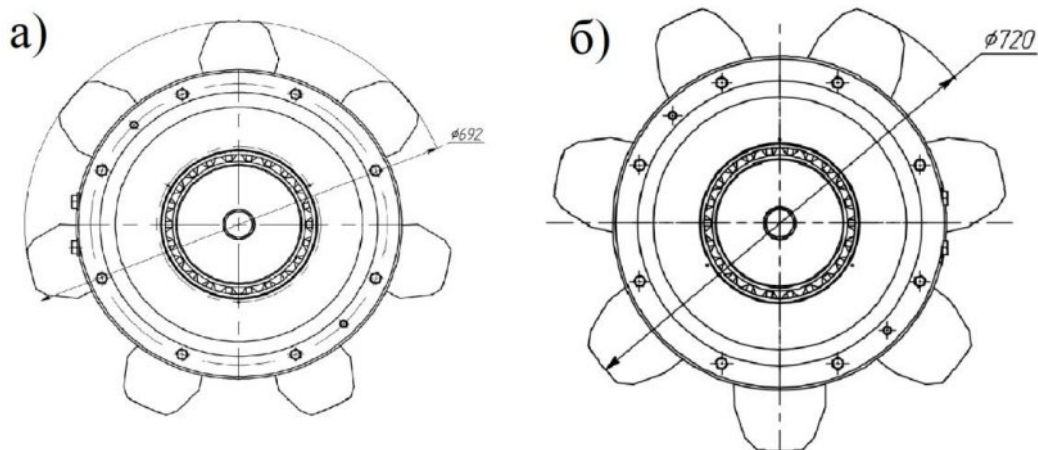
Приводные колеса: а) А-3810; б) А-4210
